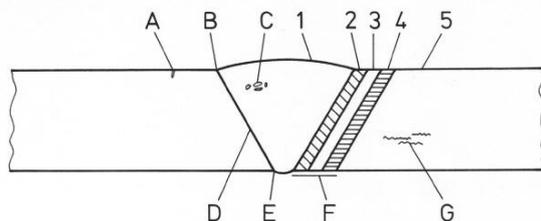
Begriffsbestimmung für Stumpfschweißnähte
